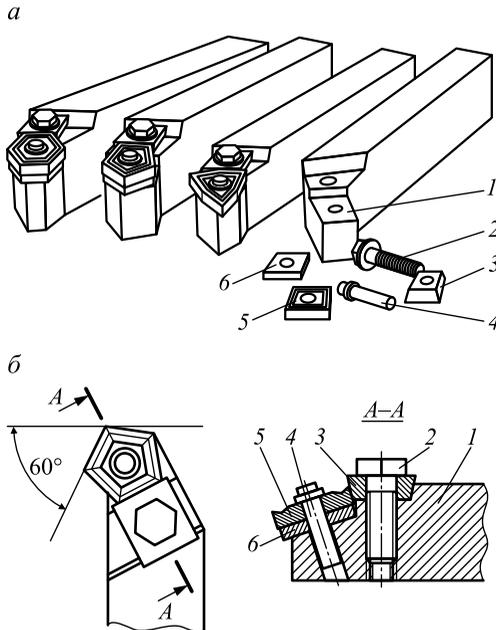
Резцы с многослойными пластинками из твердого сплава:
